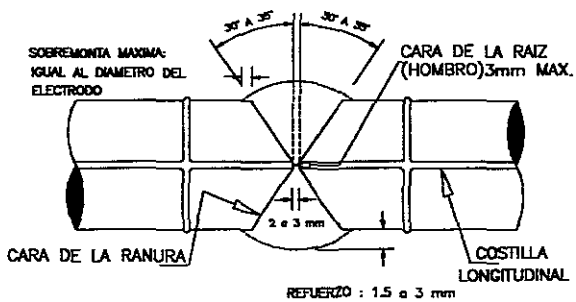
Junta a tope para calificación de soldadores en placa con espesor de 9.5mm
